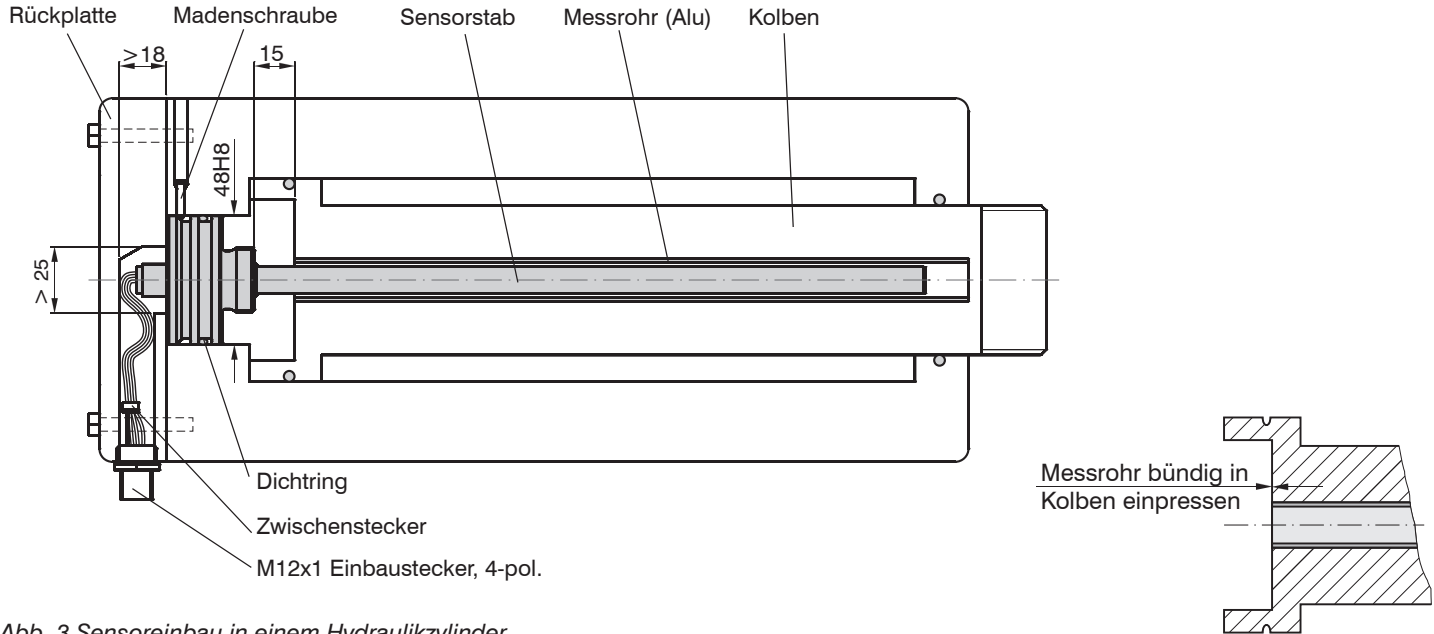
Sensoreinbau in einem Hydraulikzylinder
